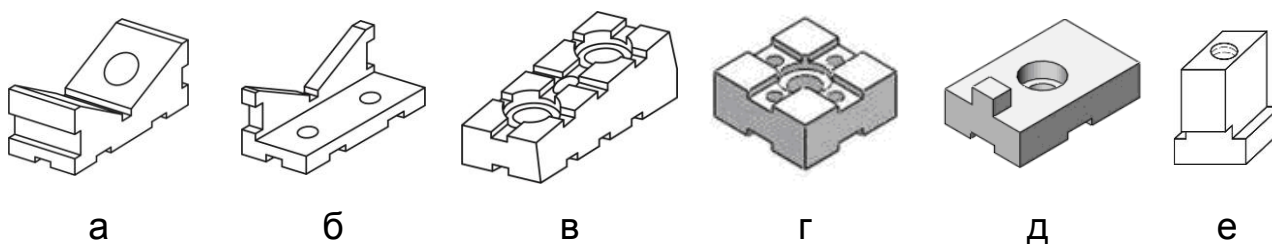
Приклади установлювальних елементів: а – призма широка; б – призма вузька; в – опора клиноподібна; г – опора плоска; д – установ для фрези; е – шпонка Т-подібна
